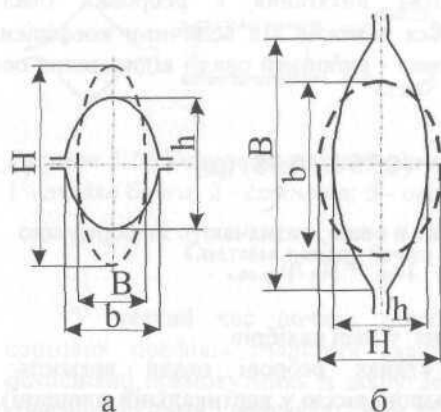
Система калібрів: а - овал - ребровий овал; б - ребровий овал-овал
